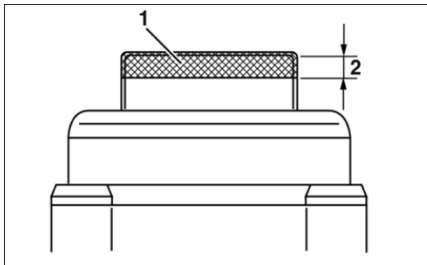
Zona de pintado para el borde cilíndrico de la membrana del sensor
